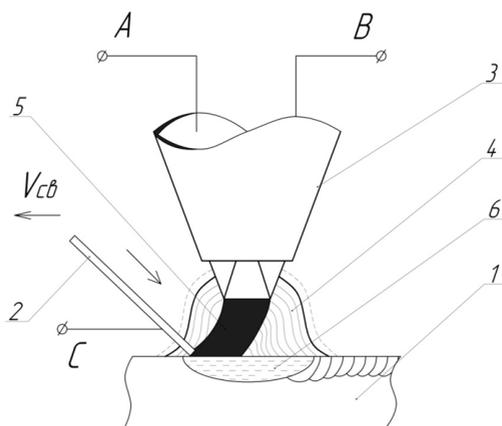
Схема сварки трехфазной дугой неплавящимся электродом:
